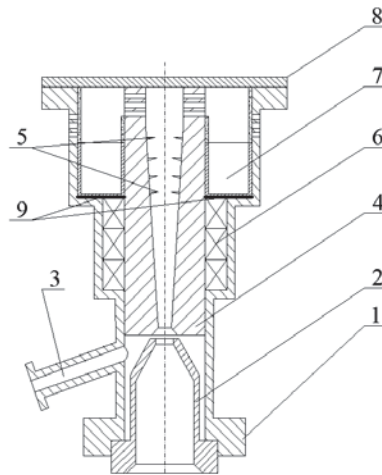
Ротаційний пиловіддільник: 1 – корпус; 2 – сопло високонапірного потоку; 3 – патрубок низьконапірного потоку; 4 – дифузор; 5 – лопаті дифузору; 6 – підшипники; 7 – циліндричний фільтр; 8 – кришка пиловіддільника; 9 – герметичне ущільнення; 10 – отвори у дифузори; 11 – отвори у корпусі.
